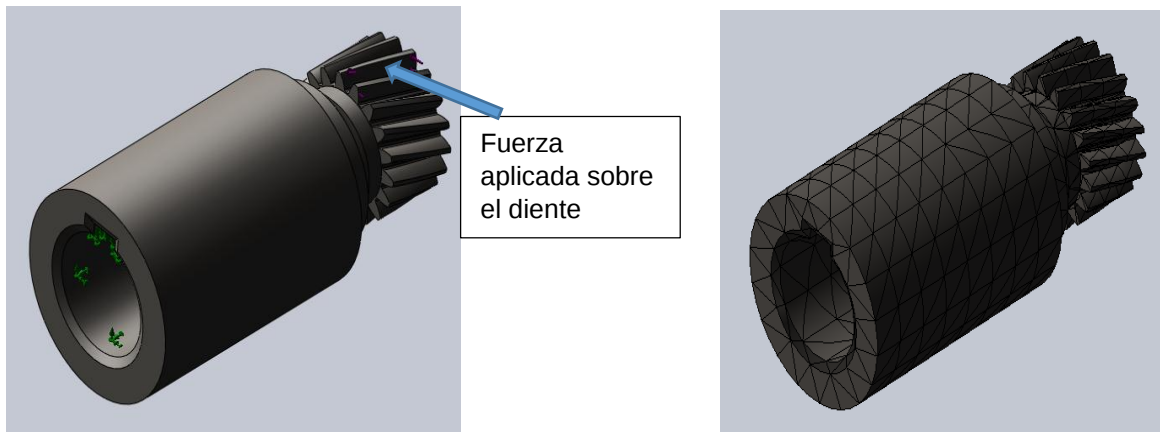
a). Condiciones de frontera para el piñón dentado
